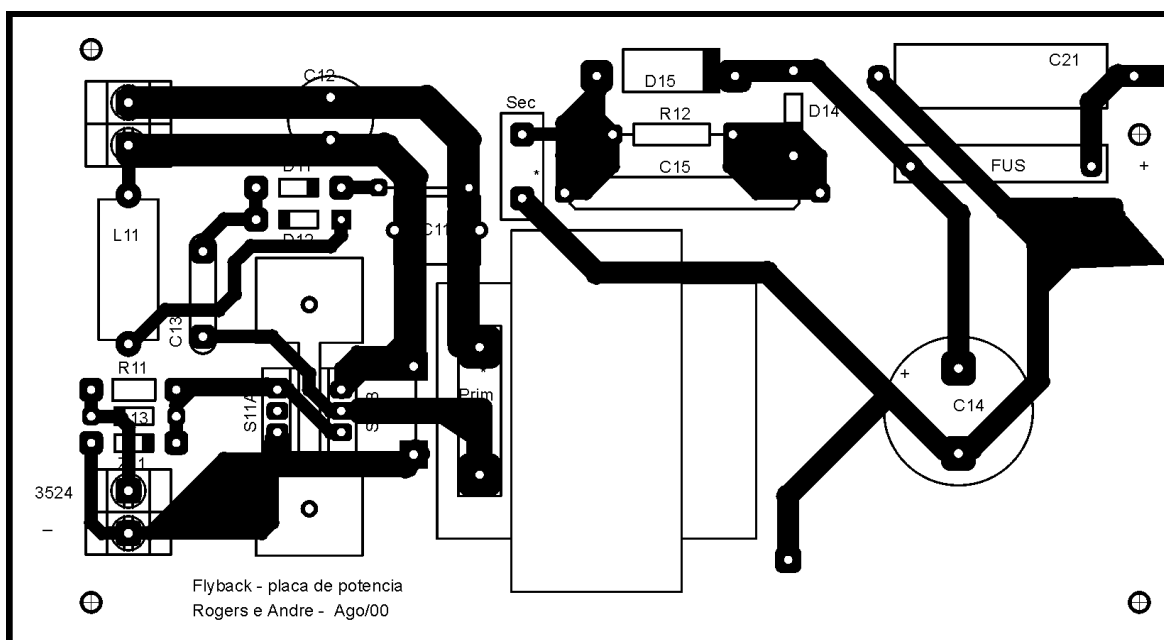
Placa de circuito impresso do conversor flyback.
